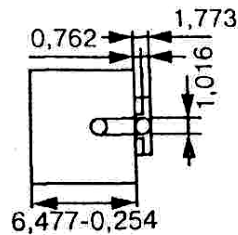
Конструкция, габаритные и присоединительные размеры корпусов низкоомных резисторов
